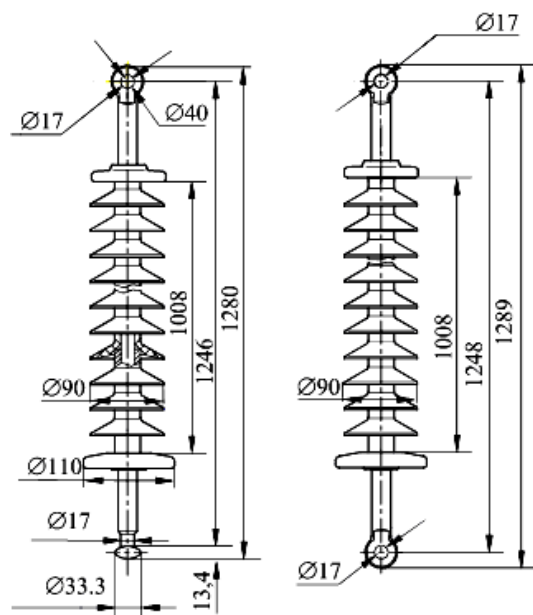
Конструкція композиційного ізолятора ЛК-70/ 110-3
